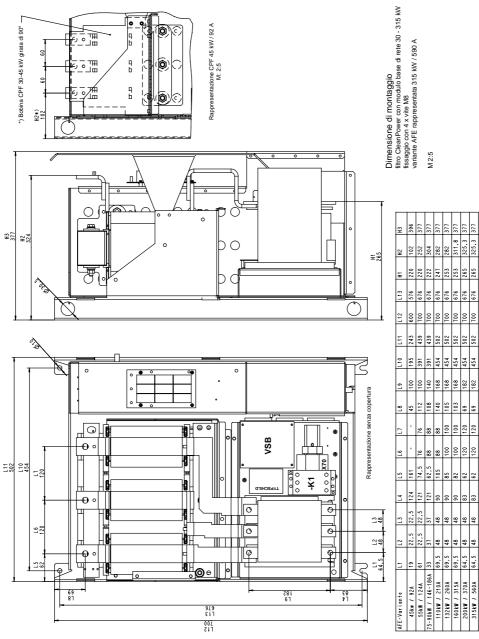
Esempio della grandezza J: dimensione di montaggio modulo di base di rete AFE con filtro CleanPower
